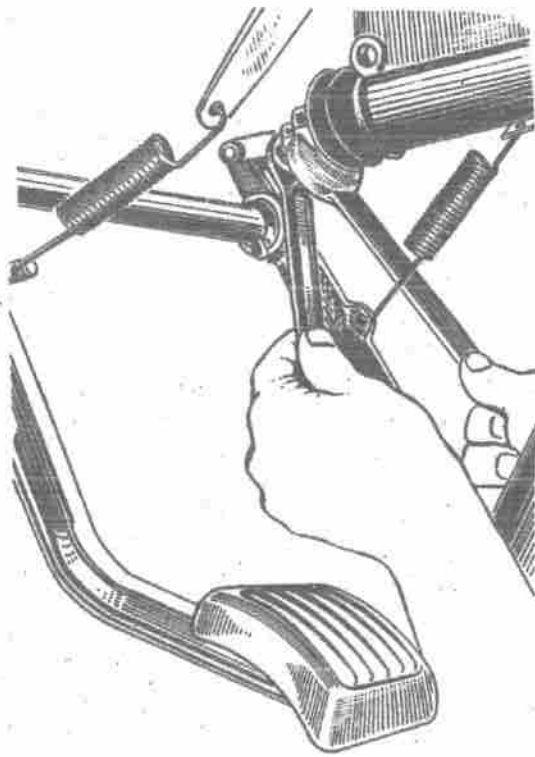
Einstellen des Spiels zwischen Kolbenstange und Kolben des Hauptbremszylinders
